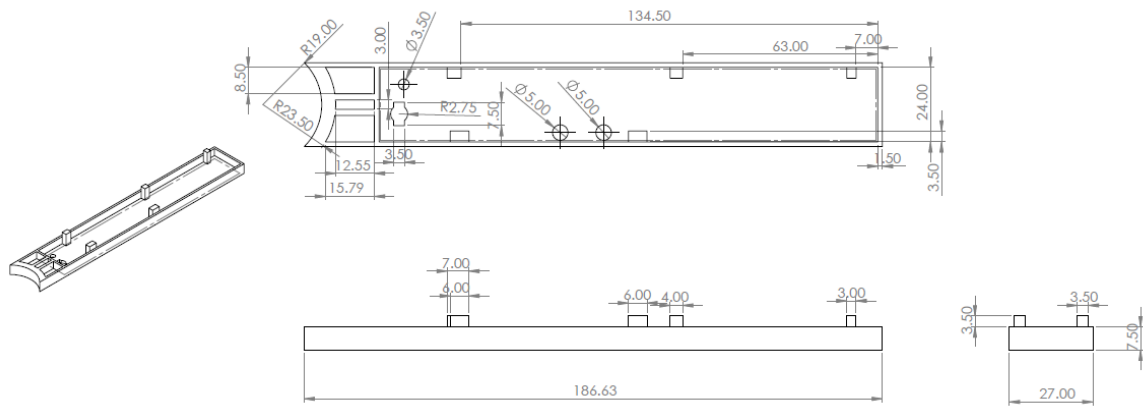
Dimensiones de pieza que cubre el circuito electrónico.
